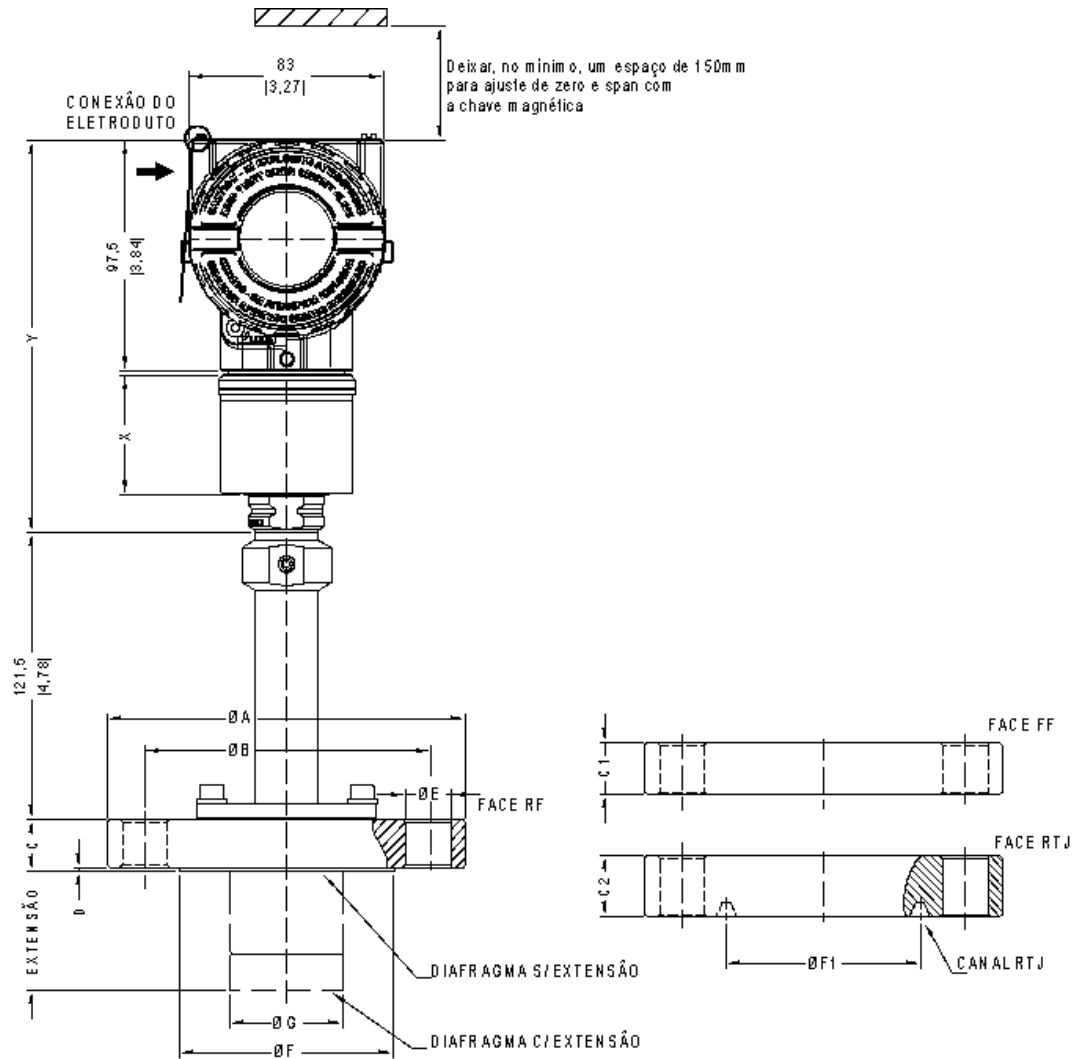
(a)- Desenho Dimensional de Montagem do LD291
